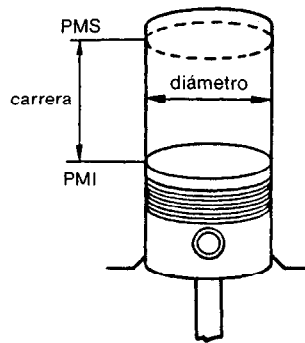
El diámetro y la carrera de un cilindro de un motor
